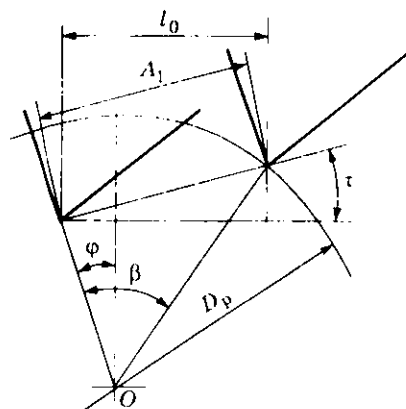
Схема определения минимально необходимой длины рабочей части фрезы для нарезания храповых колес
